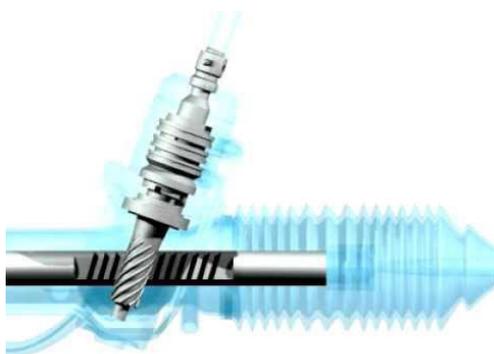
Рулевой механизм типа шестерня-рейка
